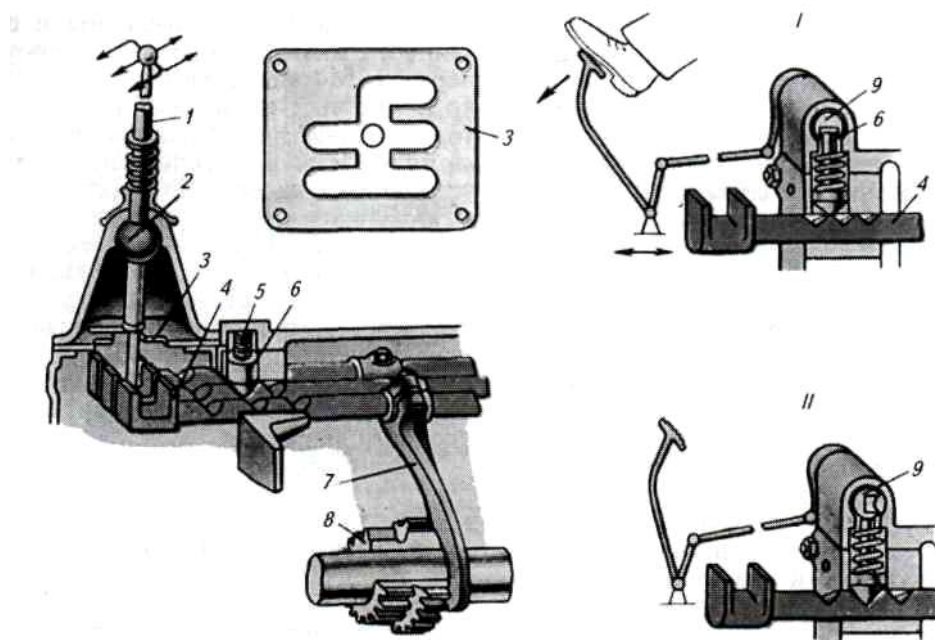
Механизм переключения и блокировки коробки передач:
